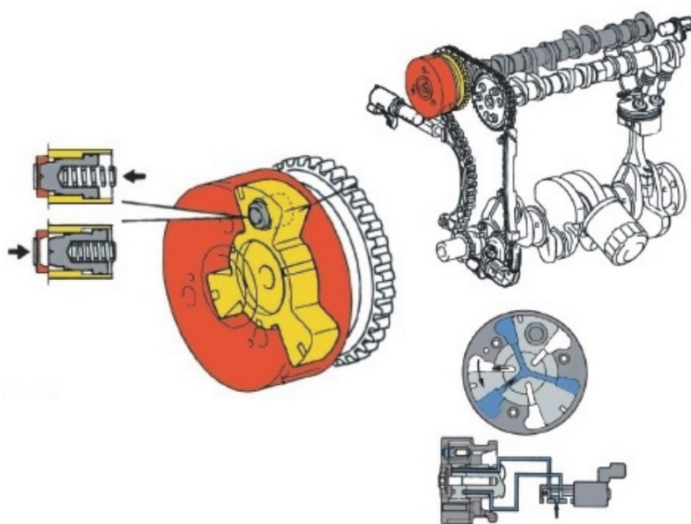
Systém Double-Vanos a Valvetronic od BMW
